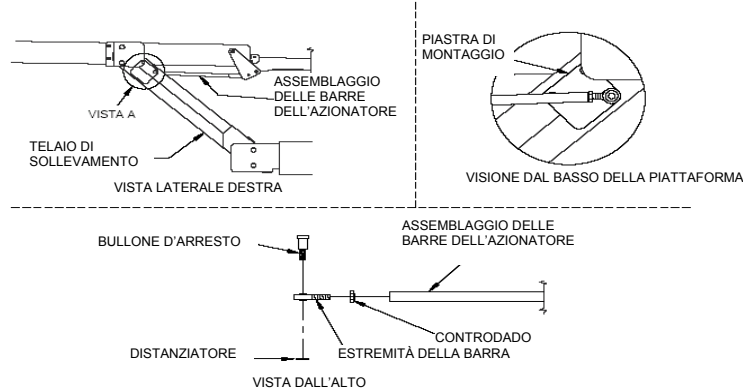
ASSEMBLAGGIO DELLE BARRE DELL'AZIONATORE DELLA PIASTRA DI FISSAGGIO
